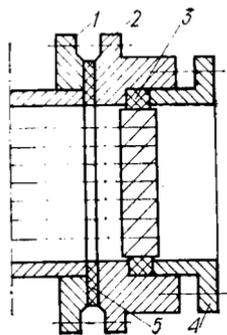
Сальниковое приспособление для опрессовки:
